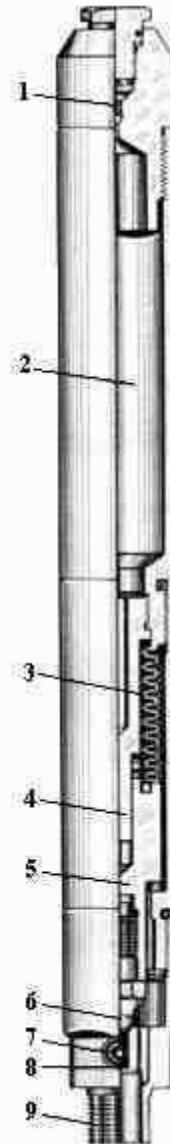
Газлифтный клапан для наружного крепления, управляемый давлением в НКТ:
